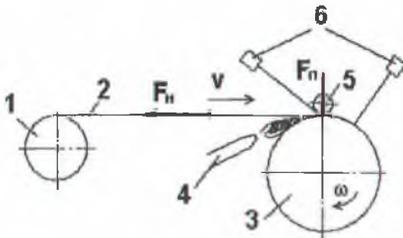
Схема намотки ленты: 1 – бобина с лентой; 2 – лента; 3 – оправка; 4 – источник тепла (газовая горелка или CO_2 -лазер); 5 – прижимной ролик; 6 – термометр
